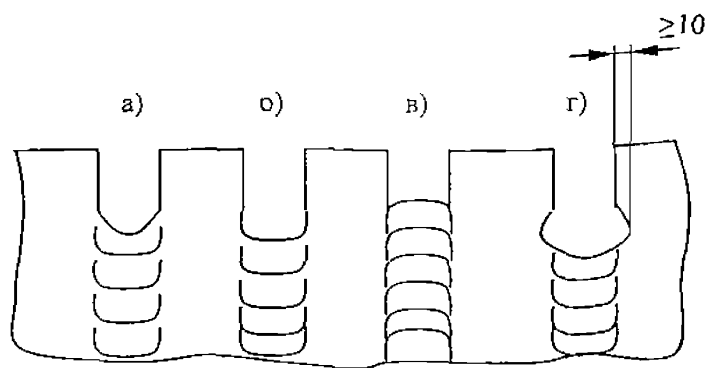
Виды формирования шва при сварке по щелевому зазору
